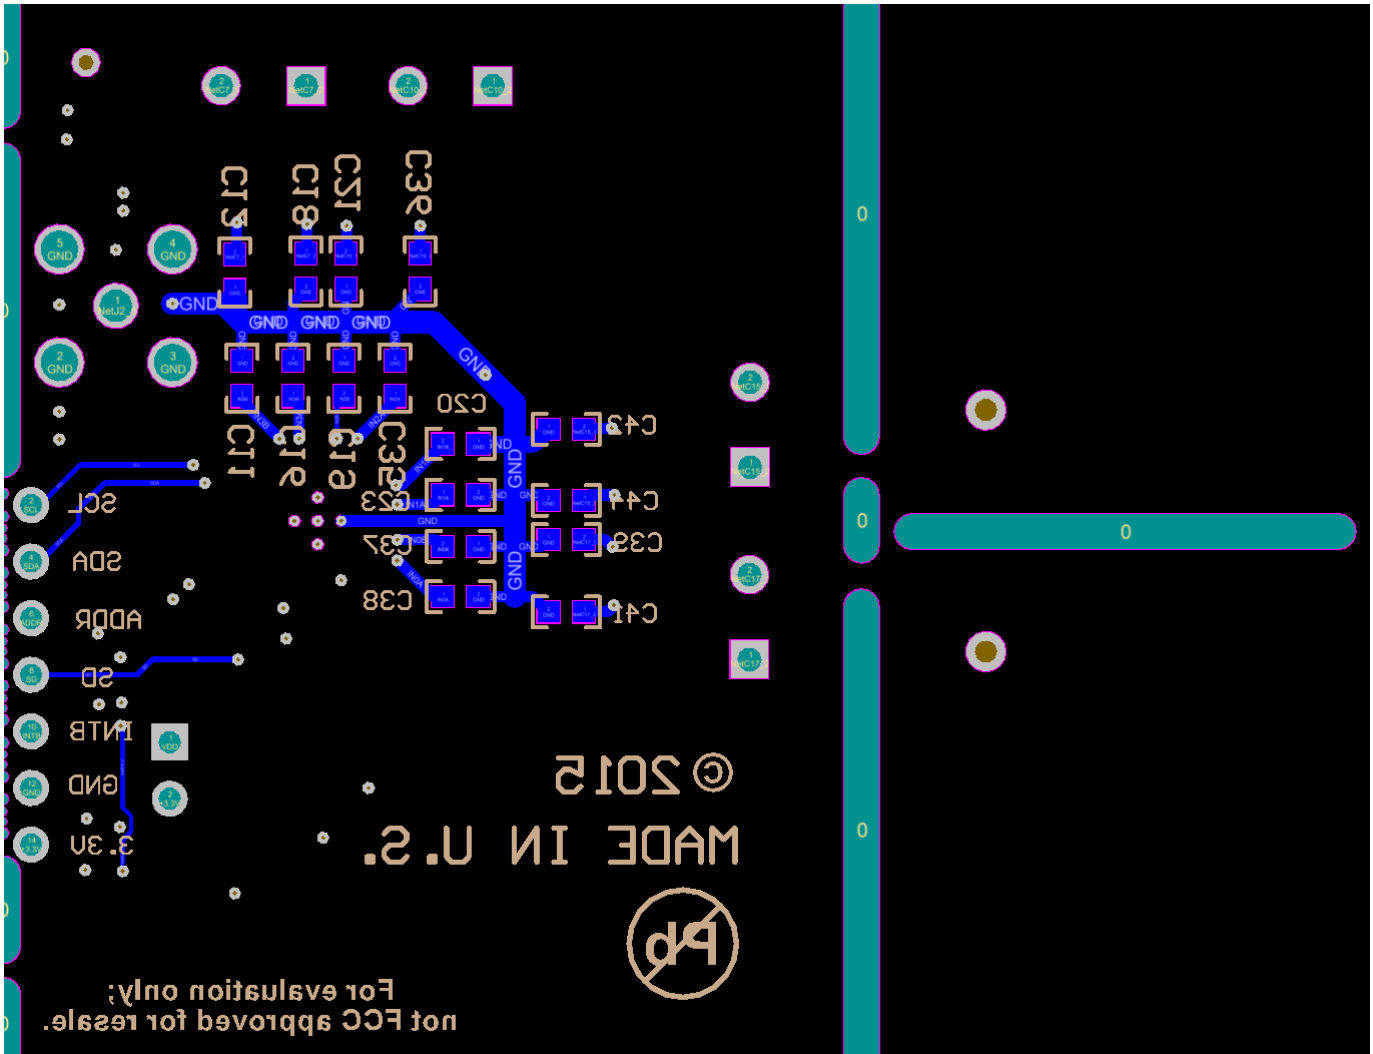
PCB レイアウトの例 : 最下層 (信号)
